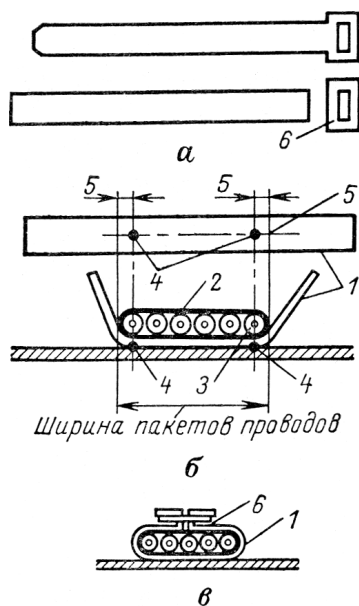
Крепление потока проводов металлической полоской на приварке: *а* — полоска металлическая с пряжкой; *б* — приварка полоски к панели; *в* — закрепление потока с помощью приварки полоски; 1 — полоска металлическая; 2 — изоляционная прокладка; 3 — провода; 4 — места точечной приварки полоски; 5 — места изгиба полоски для образования скобы (по ширине пакета проводов); б — «замок» скобы в пряжке
